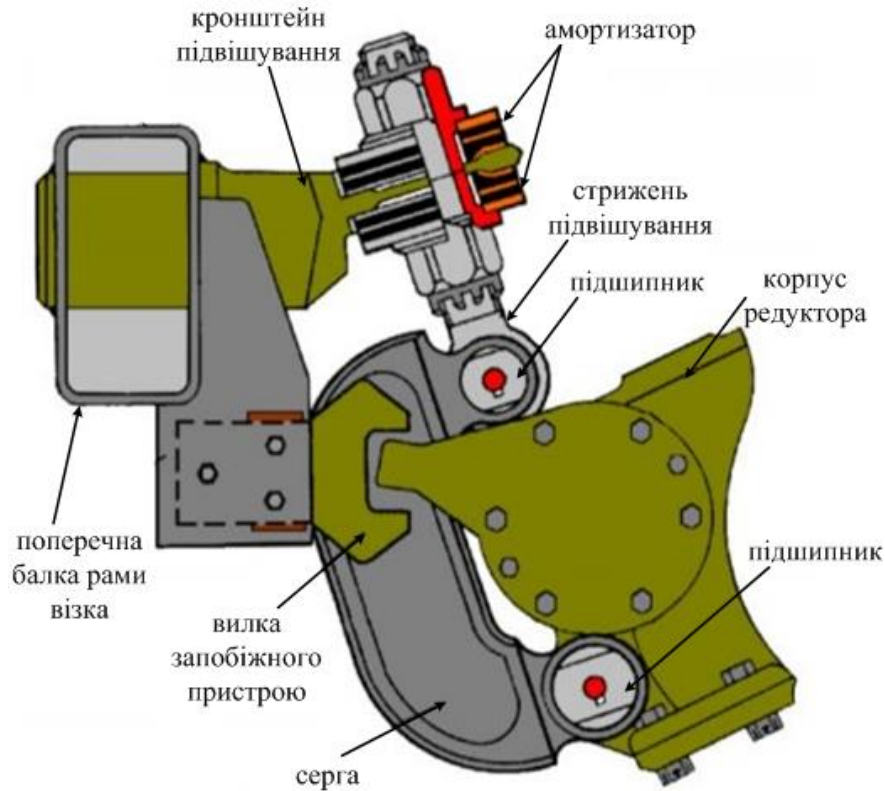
Вузол підвішування редуктора візка вагону метрополітену
